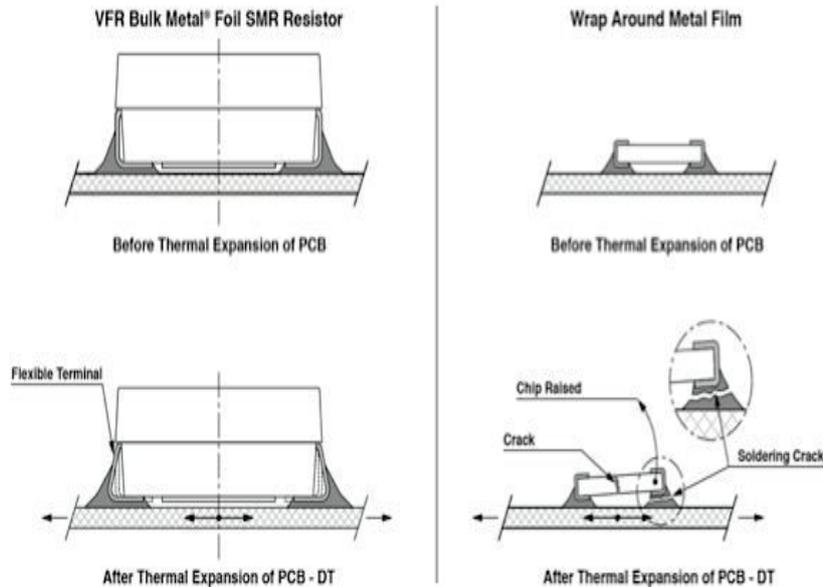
：经过热膨胀或 PCB 弯曲后带柔韧性端子的表贴精密电阻。
